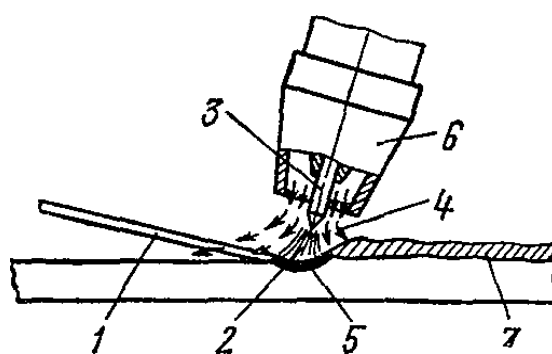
Схема аргонодуговой сварки вольфрамовым электродом. 1 — присадочная проволока; 2 — электрическая дуга; 3 — вольфрамовый электрод; 4 — защитная струя аргона; 5 — ванна расплавленного металла; 6 — горелка; 7 — сварной шов.
